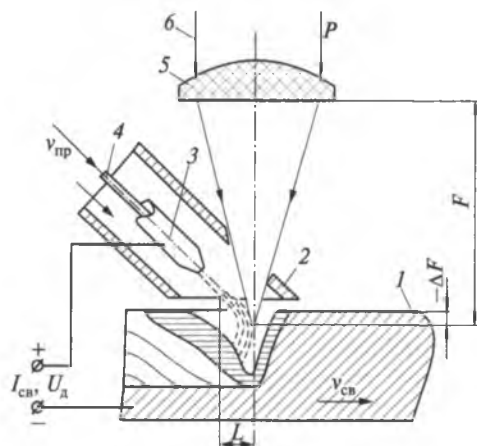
Схема гибридной лазерно-дуговой сварки алюминиевых сплавов:
